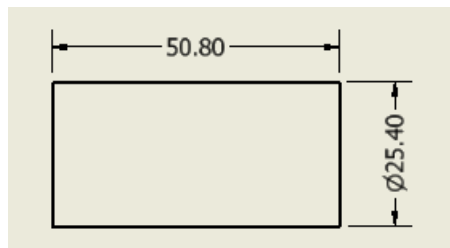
Diseño de la probeta para los ensayos mecánicos de compresión. Unidad de medida: mm
